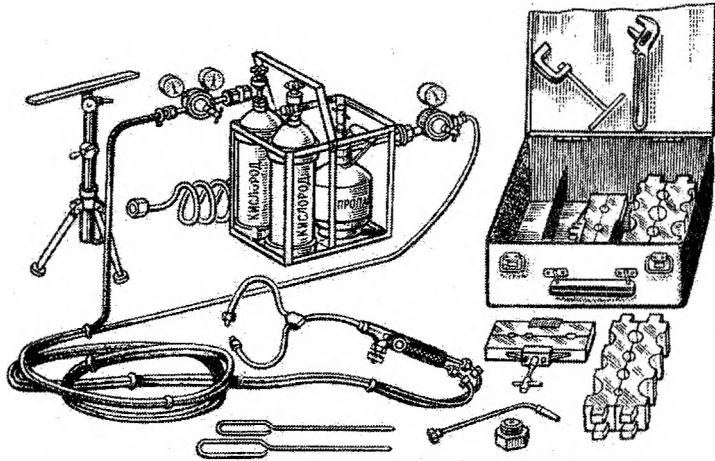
Уніфікований набір НСПУ для пайки та зварювання
